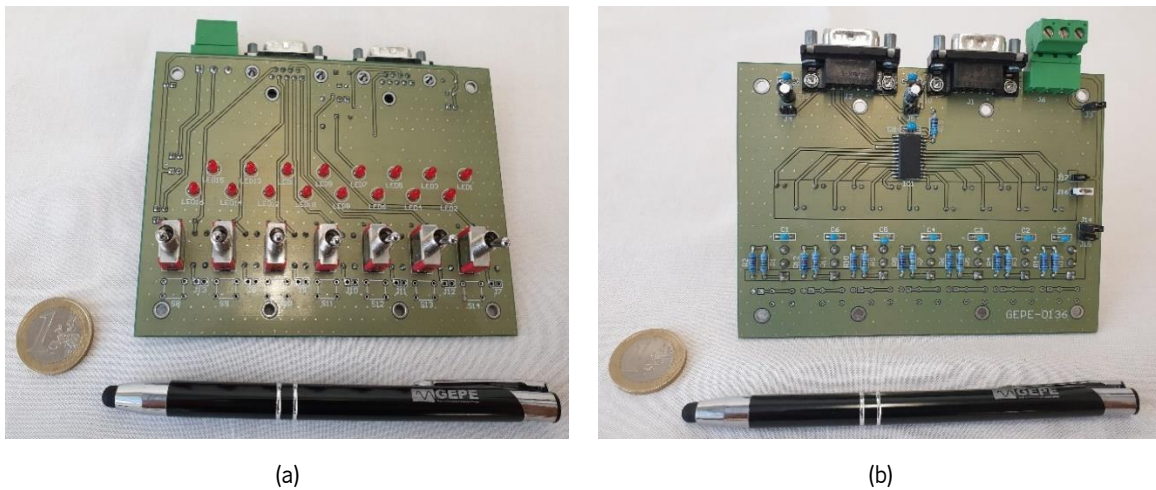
Placa de interface com o utilizador: (a) lado frontal; (b) lado traseiro.
